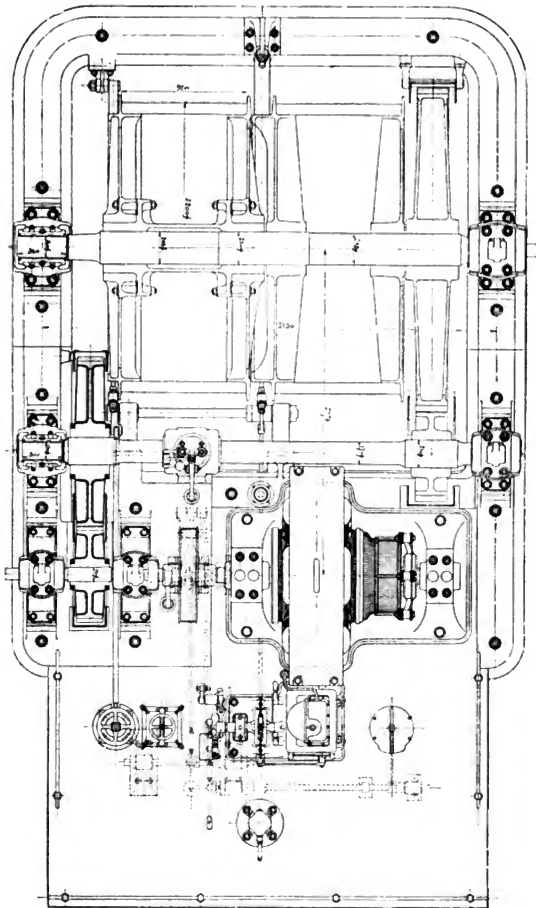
Fördermaschine. Lahmeyer. Grundriss.
